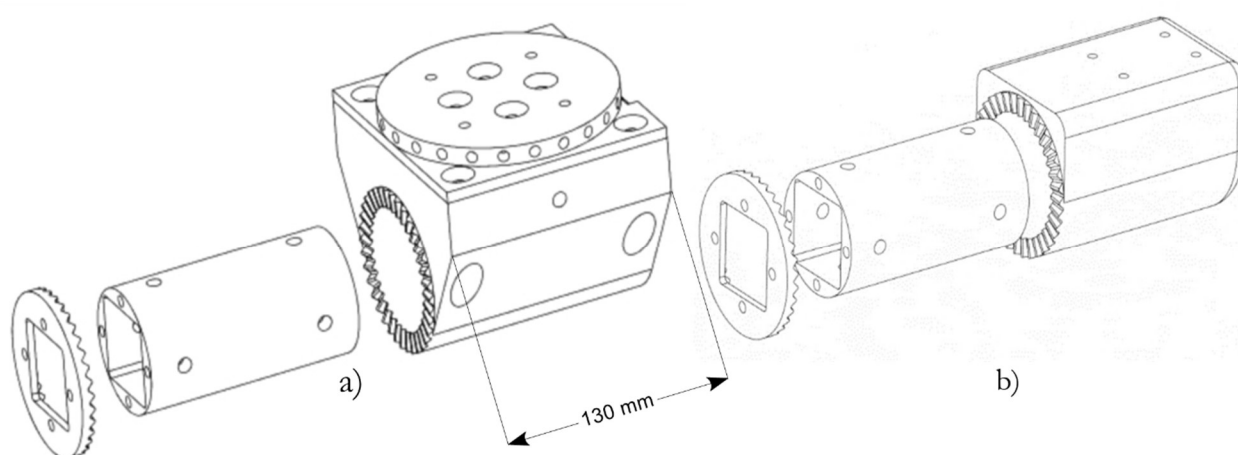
Acoplamento do módulo a) linear b) rotativo à estrutura.
